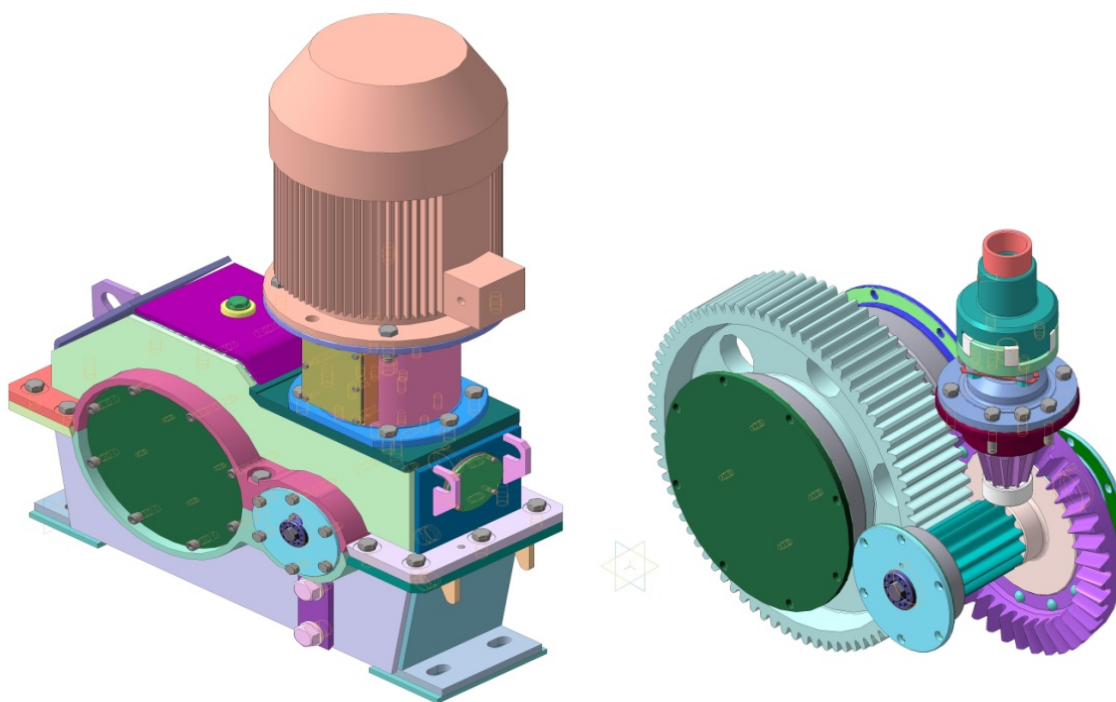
3D модель мотор-редуктора сепаратора ПБС-90/210А
